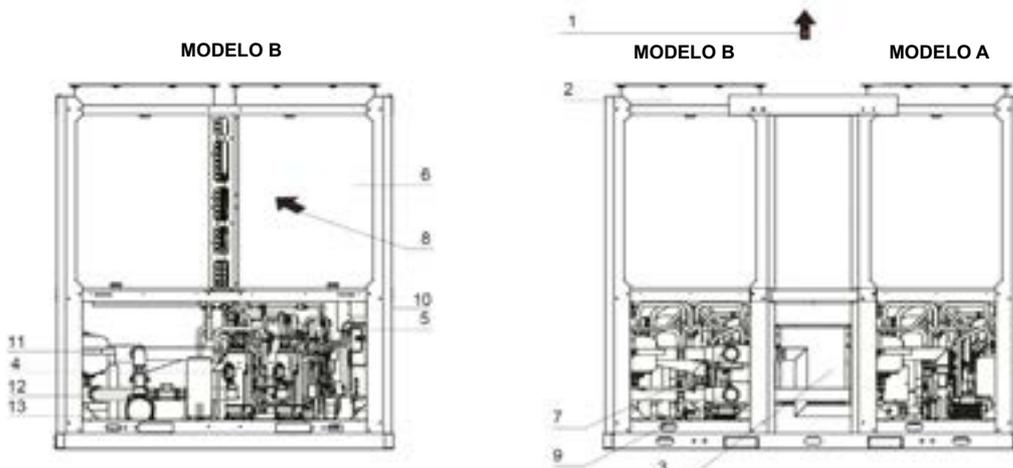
Partes principais de MUENR-180-H12T / MUENR-180-H12T(K)
